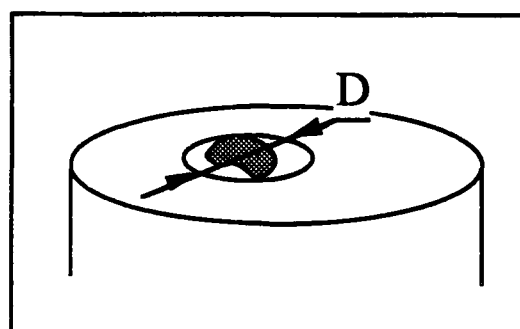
Définition de la taille  $D$  d'un défaut.
